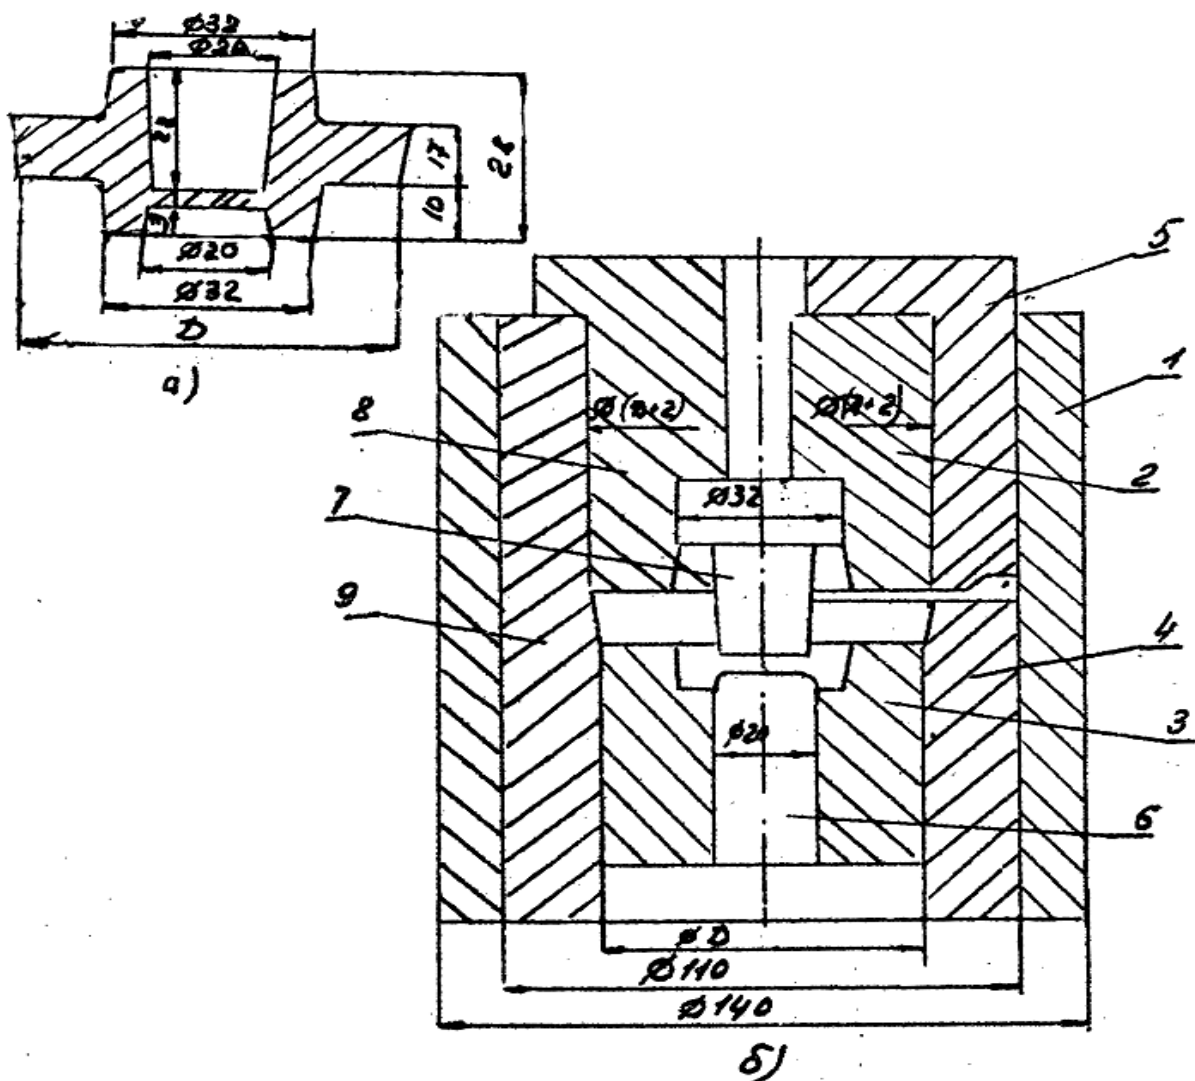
Поковка шестерни (а) и штамп для штамповки поковки диаметром 60 мм без заусенца (левая часть) и с заусенцем (правая часть): 1 – стакан направляющий; 2 – вставка верхняя; 3 – вставка нижняя; 4 – обойма нижняя; 5 – обойма верхняя; 6, 7 – вкладыши; 8 – вставка верхняя закрытого штампа; 9 – втулка промежуточная.
